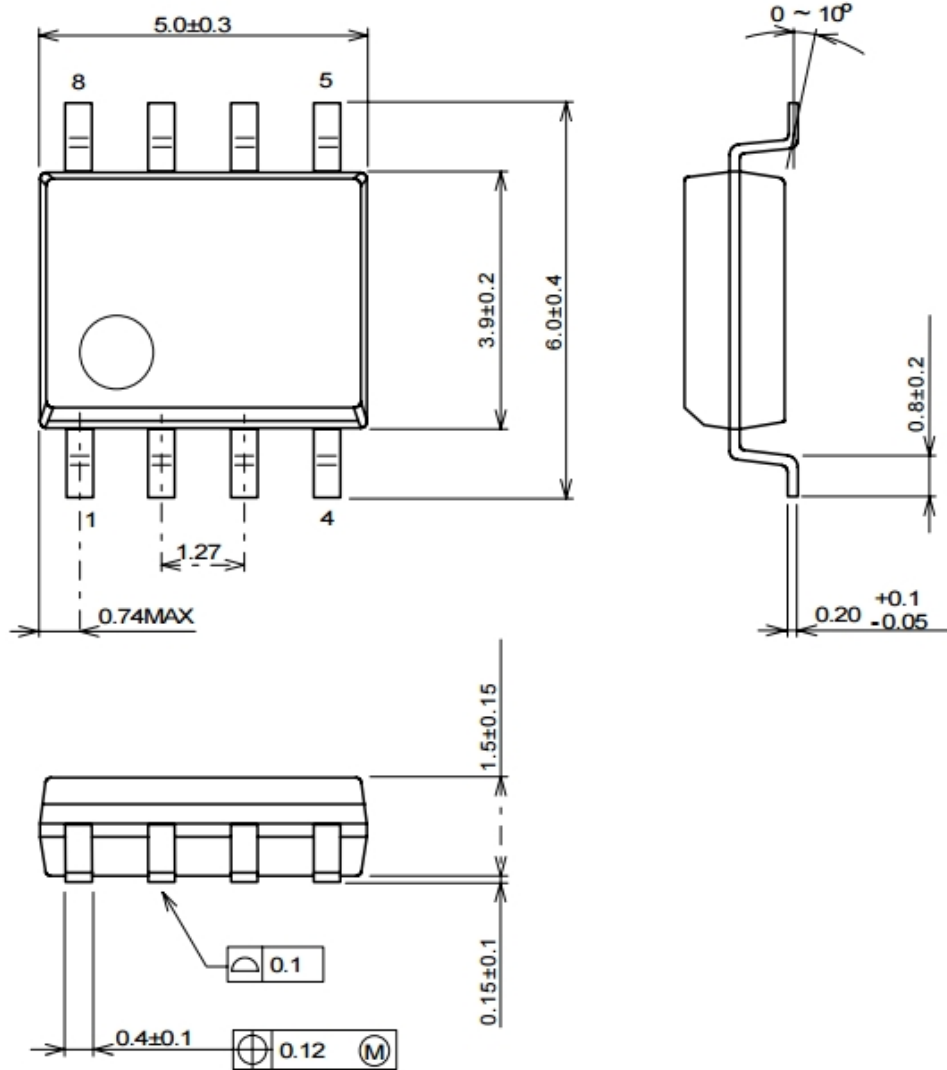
Габаритні розміри корпусу SOP-8 мікросхеми TDA2822
